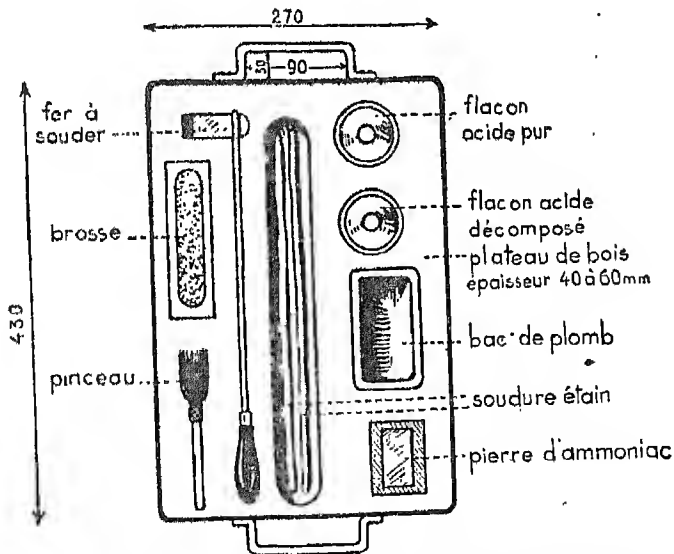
Nécessaire à souder. Tout l'outillage nécessaire pour souder est porté par un plateau épais en bois, muni de deux anses.
